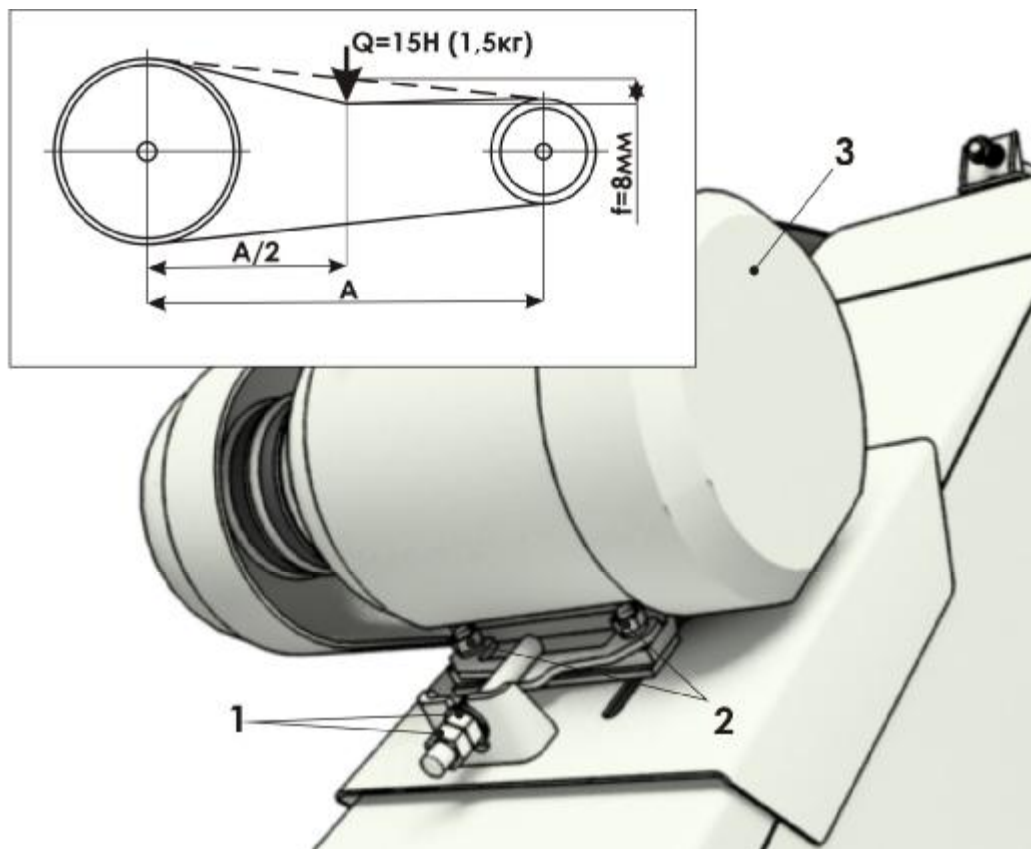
Регулировка натяжения клиноременной передачи привода загрузочного транспортера
